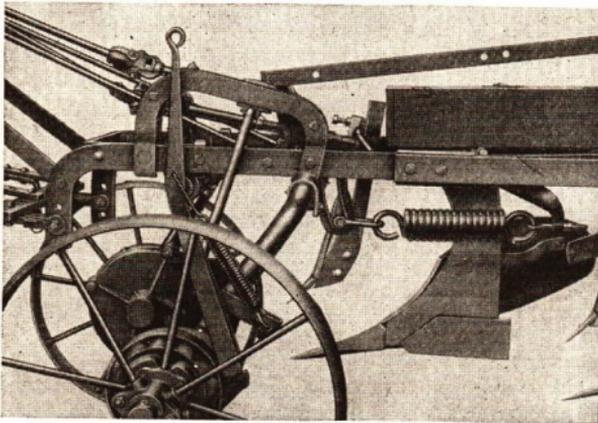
/6. Schraubenfedern (Zugfedern) an einer landwirtschaftlichen Maschine
